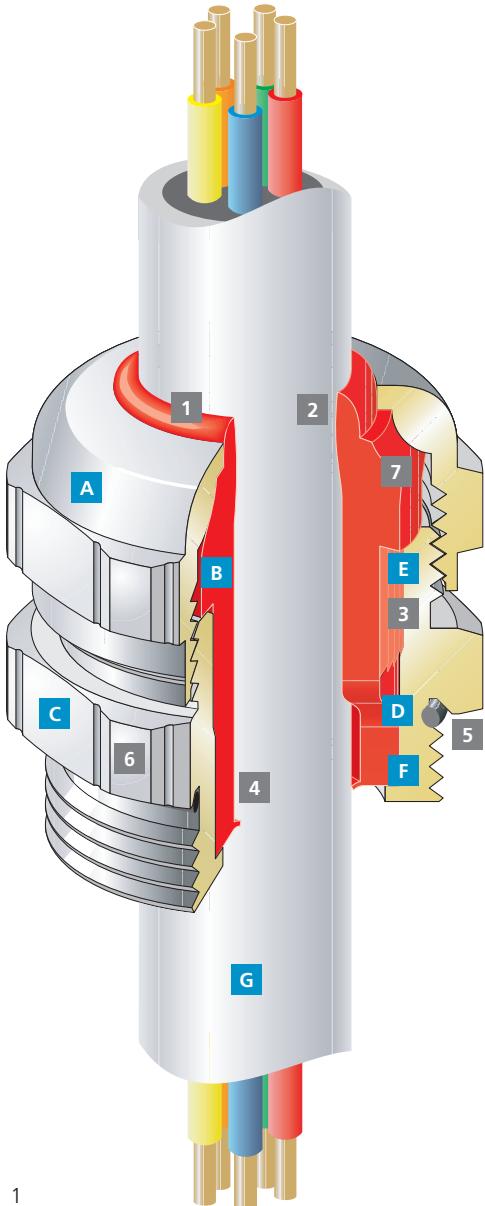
Querschnitt einer UNI Dicht®-Kabelverschraubung
